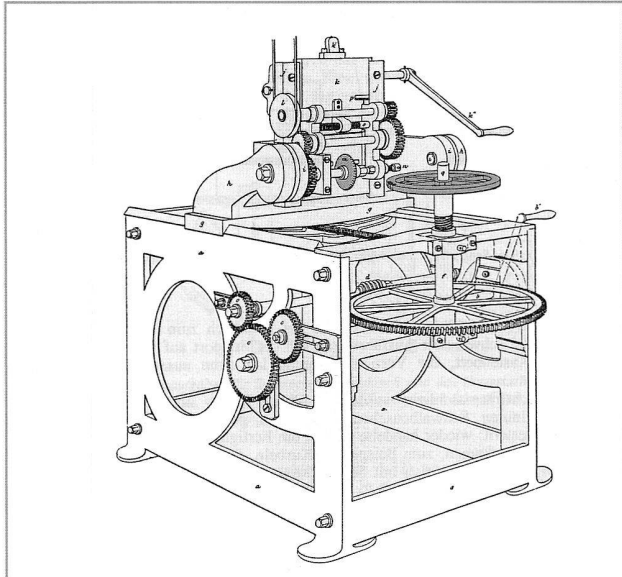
Zahnradfräsmaschine mit Kreisteilapparat und feingezahntem Fräser. (Quelle: Robertson Buchanan: Practical Essay on Mill Work and other Machinery. London 1841, Tf. 40a)
